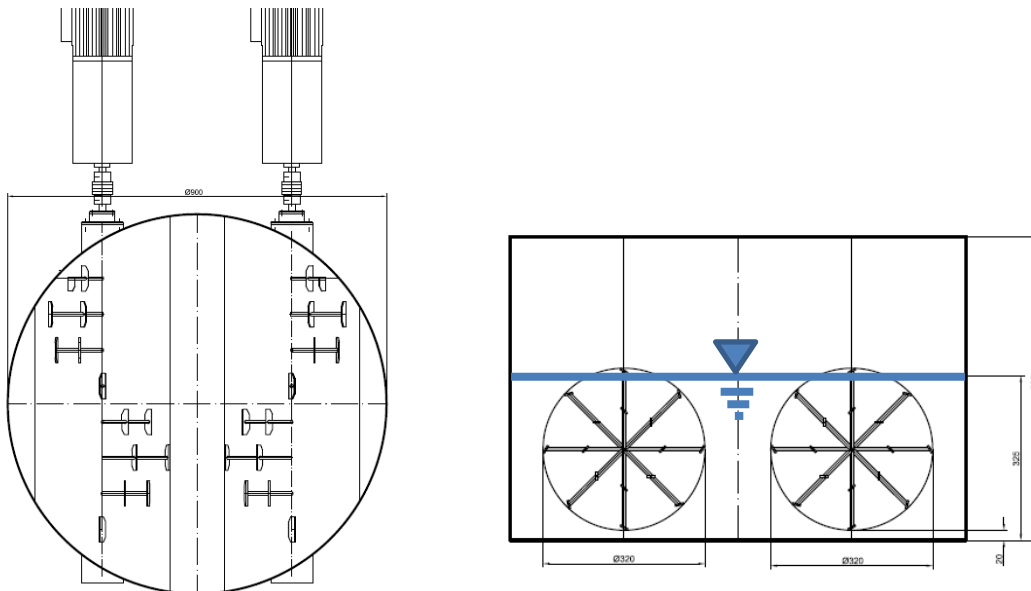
Technische Zeichnung Tomographie-Reaktor Draufsicht (links), Schnitt (rechts)
